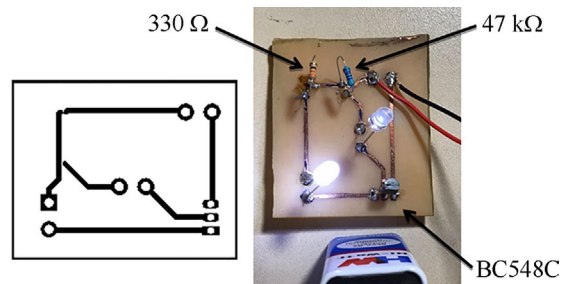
(a) Desenho para confecção da placa de circuito impresso. (b) Placa pronta, com todos os componentes soldados.
